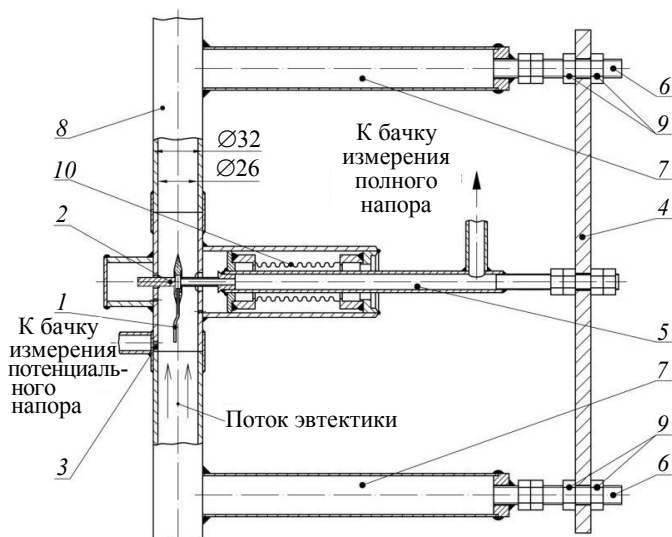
Схема датчика скорости: 1 — капиллярная трубка; 2 — зонд; 3 — отверстие измерения потенциального напора; 4 — дистанционирующая пластина; 5 — трубка соединительная; 6 — шпильки дистанционирующие; 7 — штанги опорные; 8 — труба экспериментального участка; 9 — гайки перемещающие; 10 — сифон
